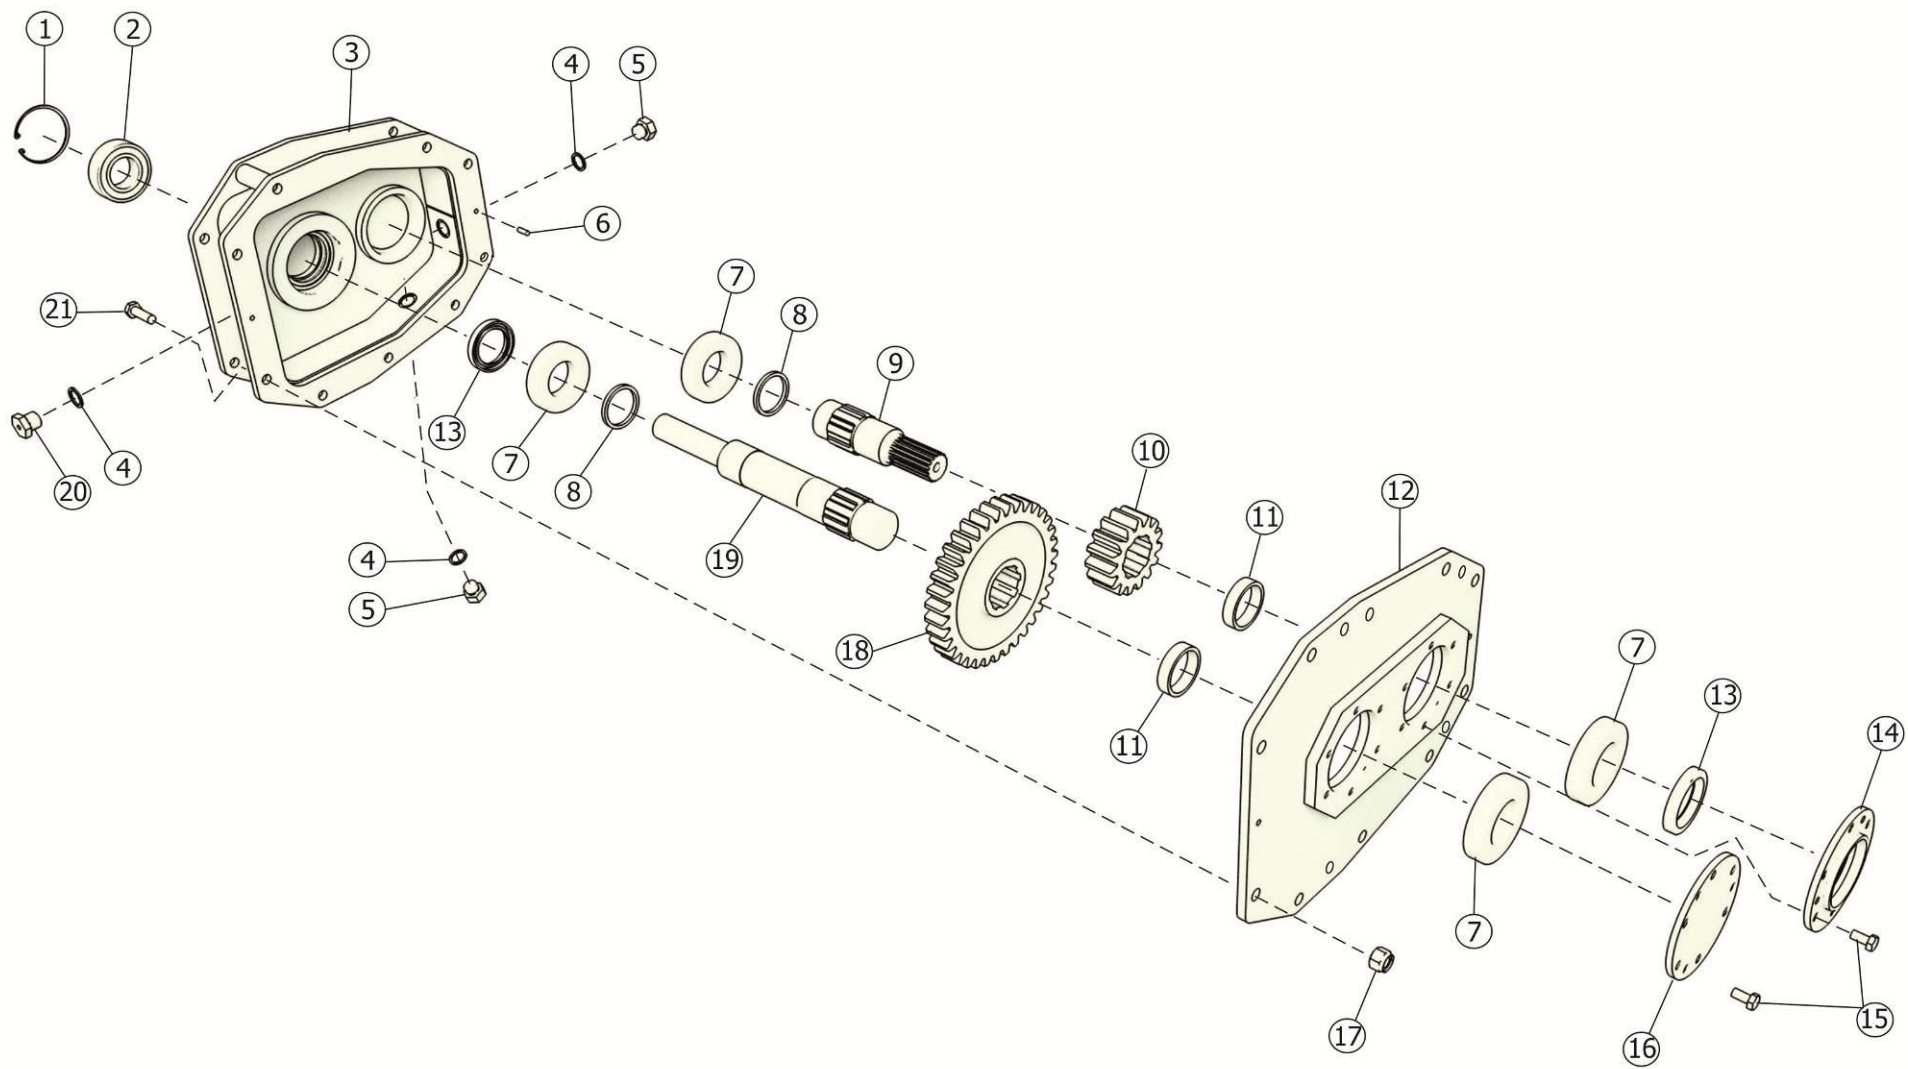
Редуктор ПФ-307.01.05.050Б
